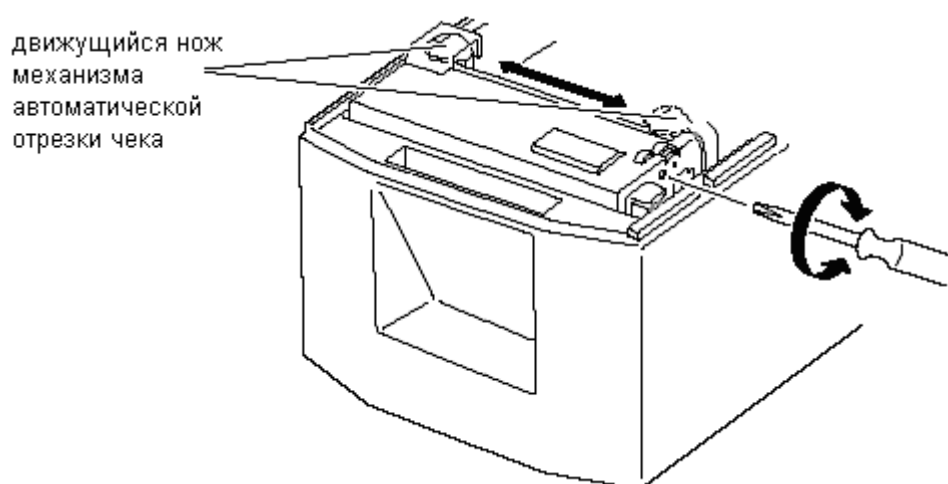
Винт регулировки ножа механизма автоматической отрезки чека
